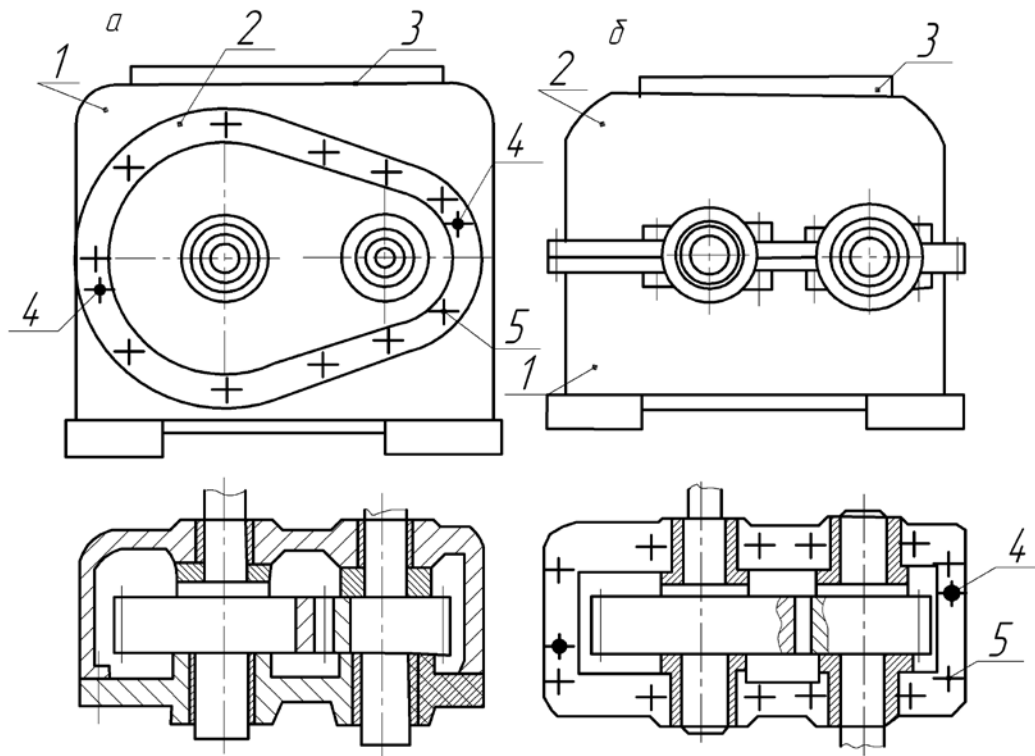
Конструкции редукторов, позволяющих осуществлять осевую (а) и поперечную (б) системы сборки
